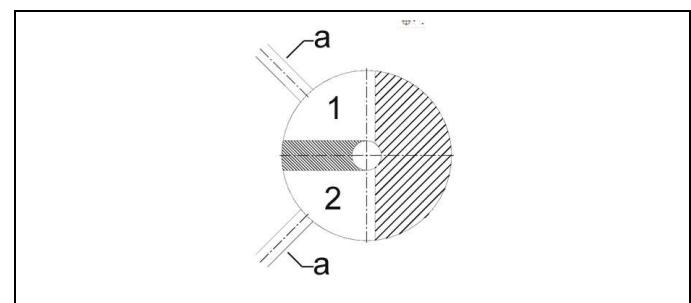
Rappresentazione posizionamento boccola di segnalazione
